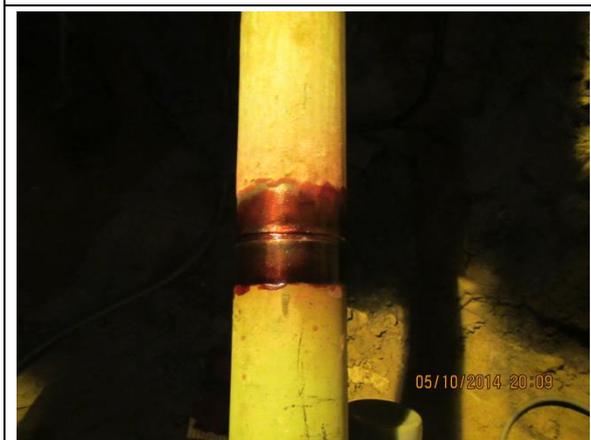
Vista del ensayo no destructivo (tintas penetrantes) practicado al niple reemplazado.
